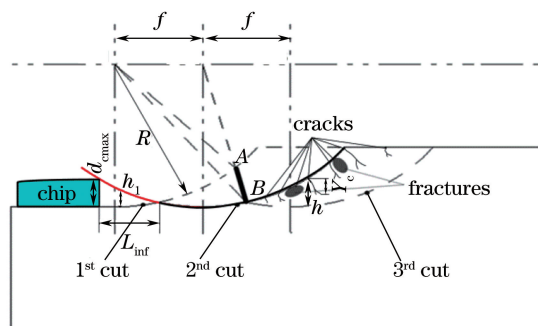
圆弧刃刀具加工引入表面缺陷的示意图
